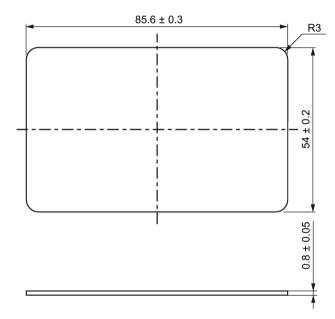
Desenho de dimensões MDS D400 (medidas em mm)
